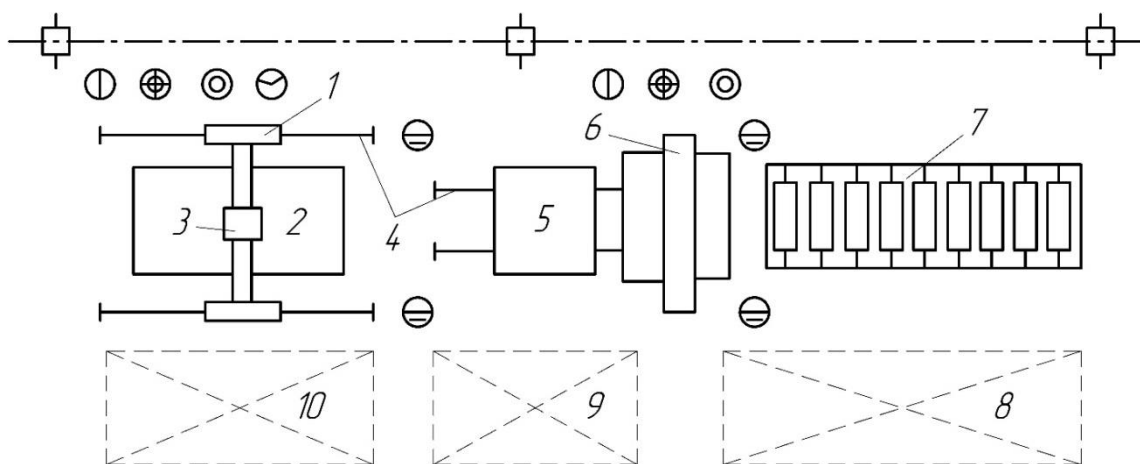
Планировка заготовительного участка резки металла разной толщины: 1 – портал самоходный; 2 – плита (стол) для резки металла; 3 – автомат-резак; 4 – направляющий рельс; 5 – тележка; 6 – гильотинные ножницы; 7 – рольганг; 8 – складочное место для исходных листов и заготовок; 9 – складочное место для разрезанного листового металла; 10 – складочное место для разрезанного толстого металла
